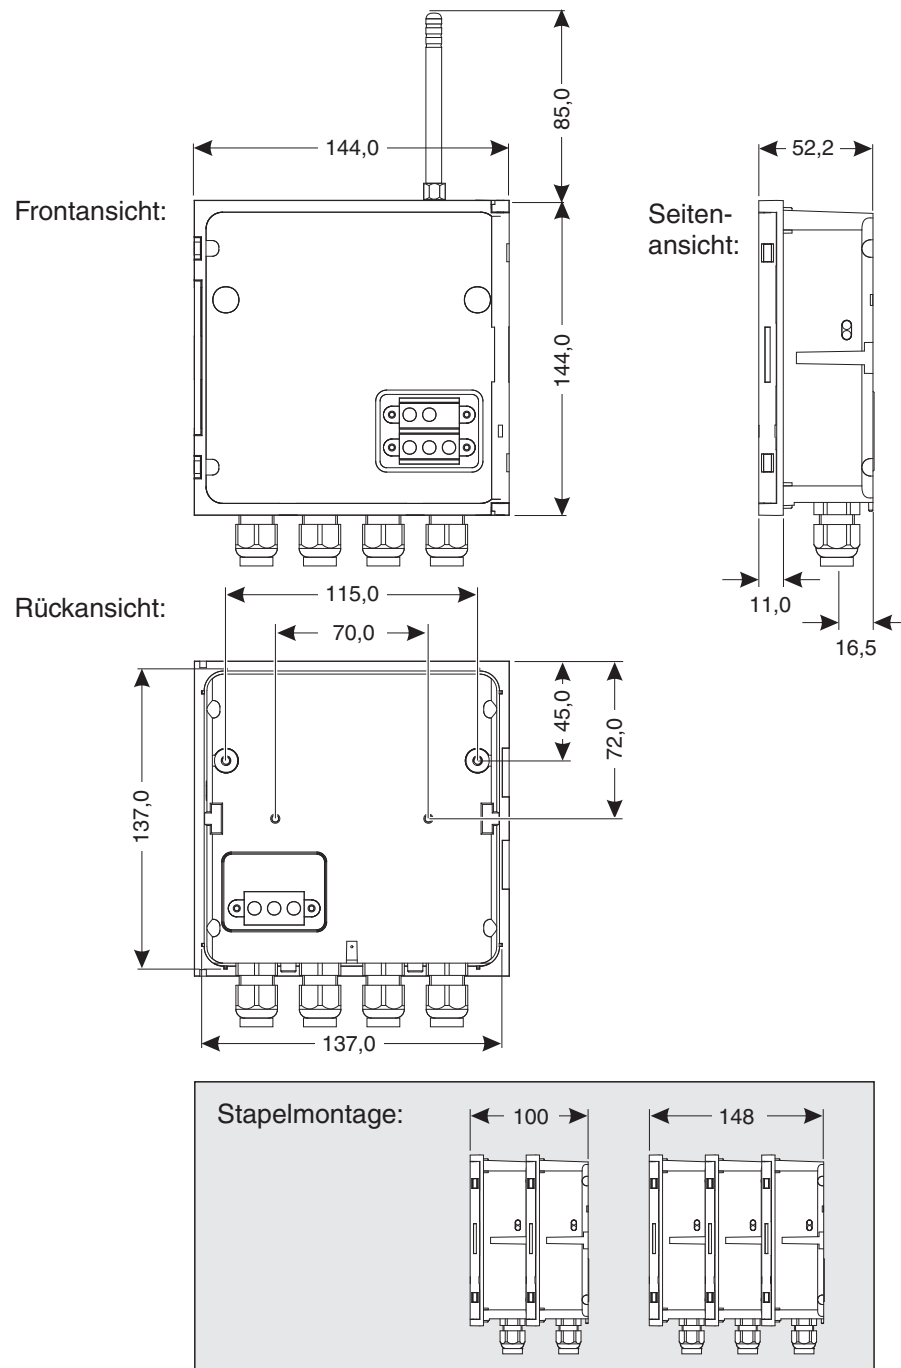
Maßzeichnung MIQ Modul (Maße in mm)
